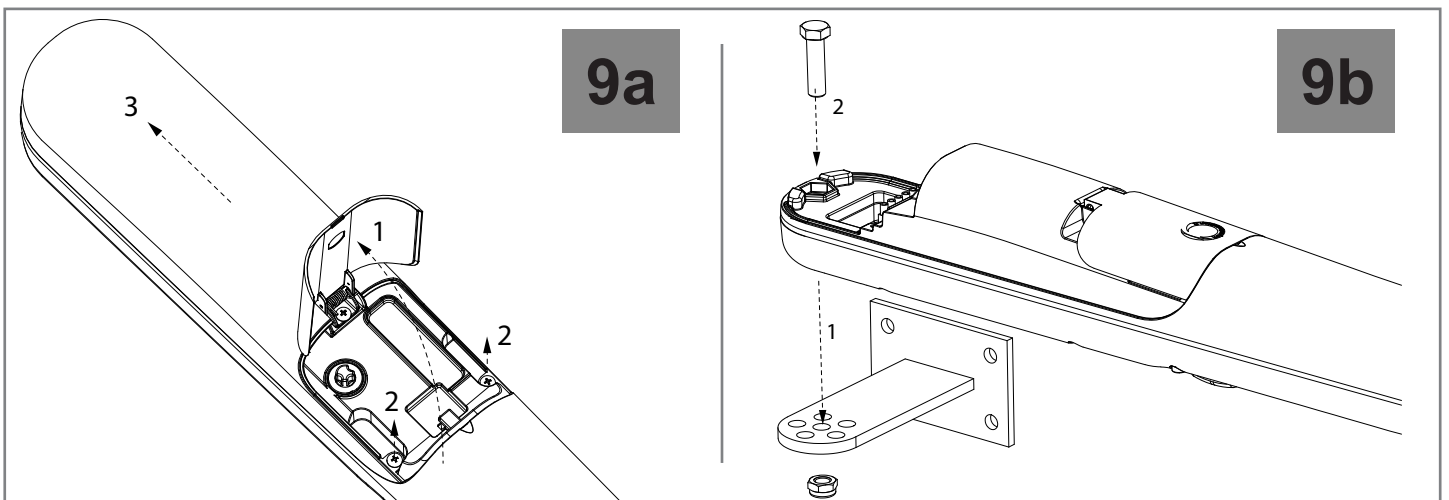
IT - Fissaggio motoriduttore e staffa anteriore
